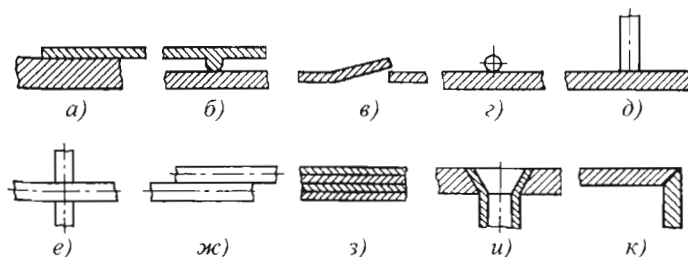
Основные типы сварных соединений металлов:
